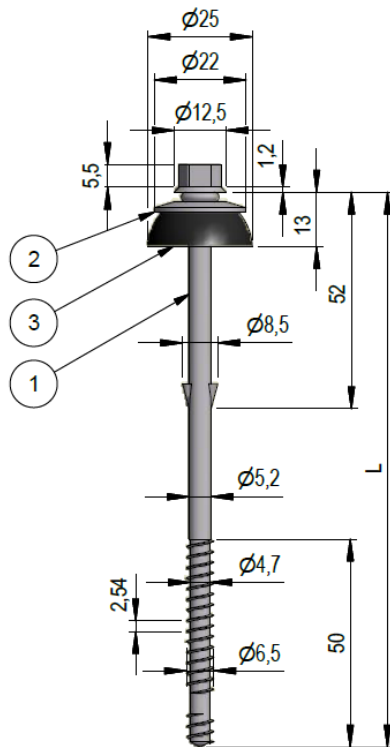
Pilzkopfdichtung für Stahlhaken und Sechskant-Holzschrauben
